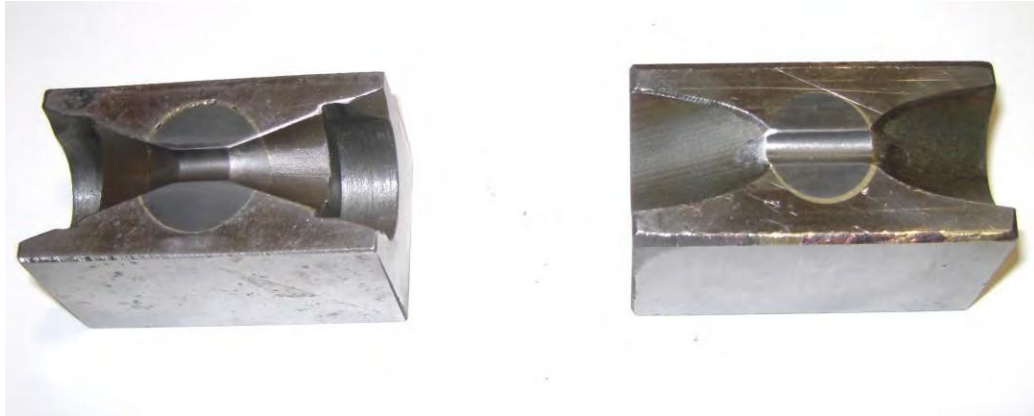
Ковочные рабочие стальные бойки с твёрдосплавными вставками 2-х исполнений
